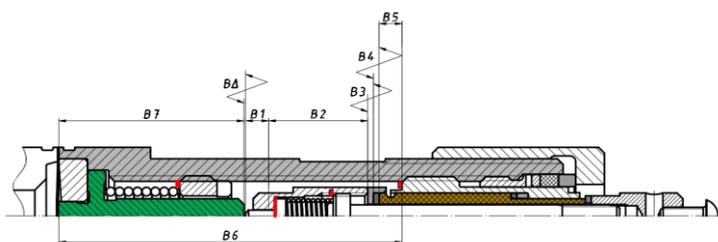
Вариант схемы размерной цепи В, обеспечивающей при сборке достижение точности зазора между исполнительными поверхностями СП
